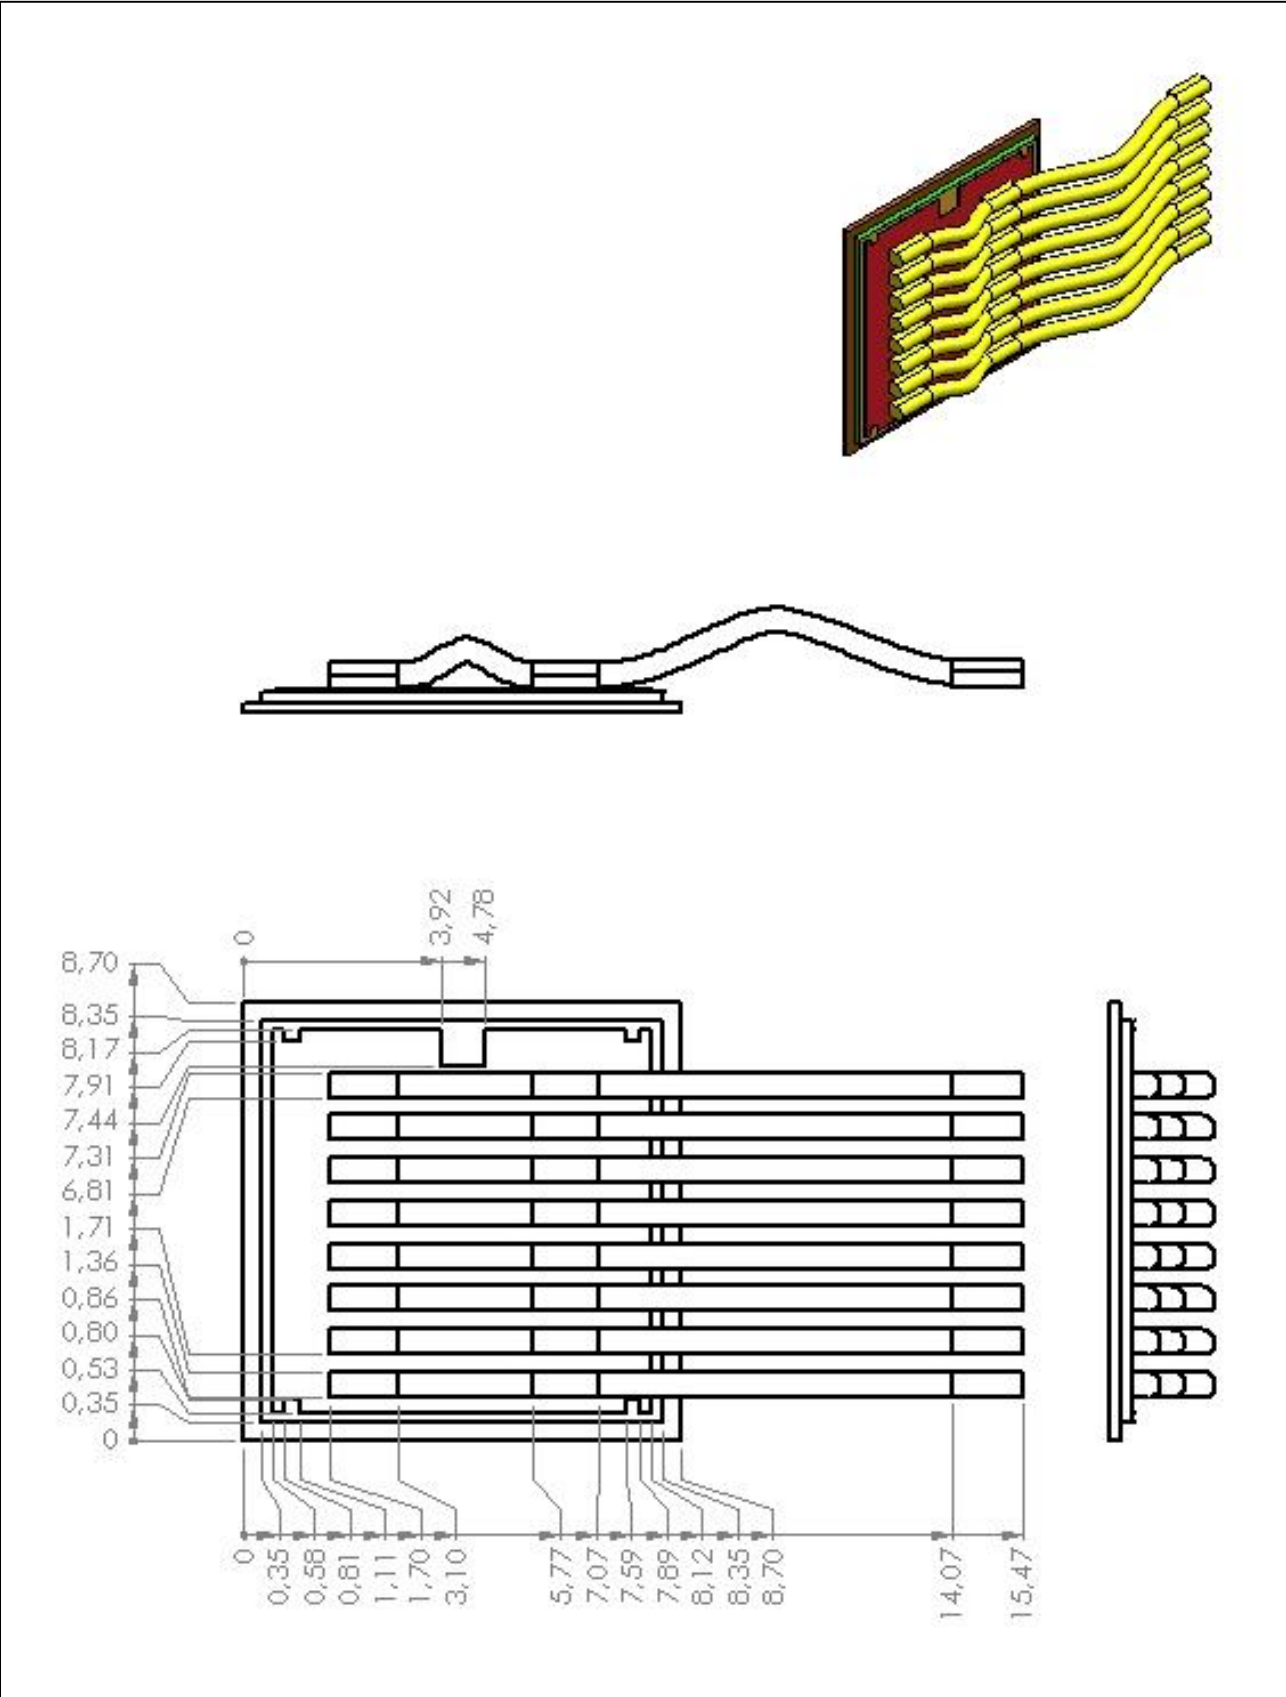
Dimension du MOSFET et emplacement des fils
